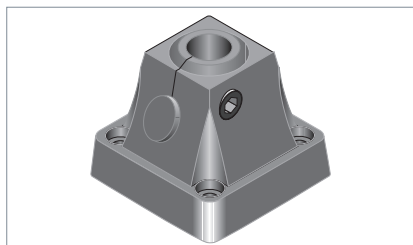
Elemento di fissaggio, fissaggio mediante viti.
